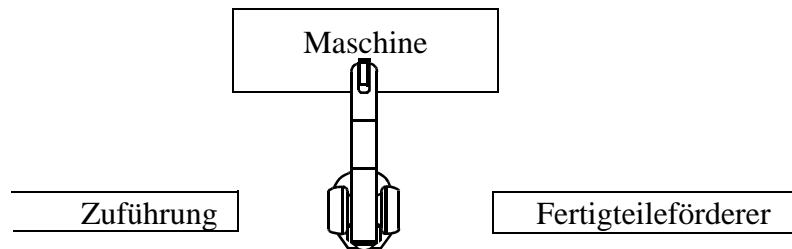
Der Manipulator beschickt eine Maschine, die das Werkstück bearbeitet.
